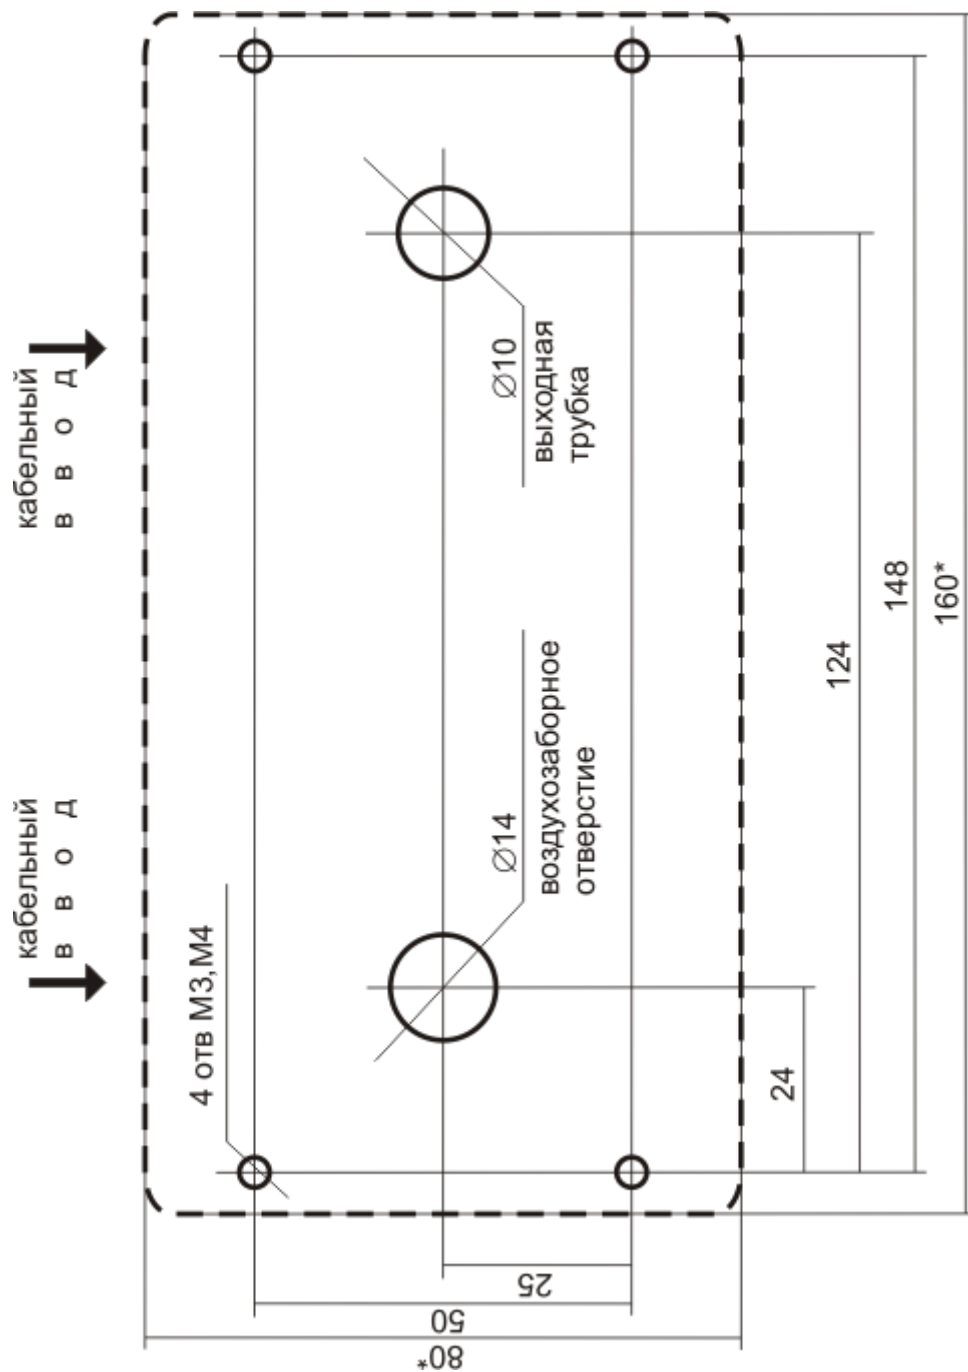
Разметка крепления извещателей пожарных газовых проточных
